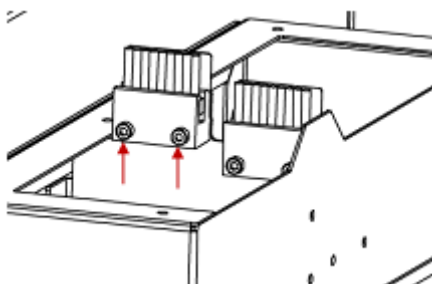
Крепежные винты устройства очистки для рабочего конца T0
